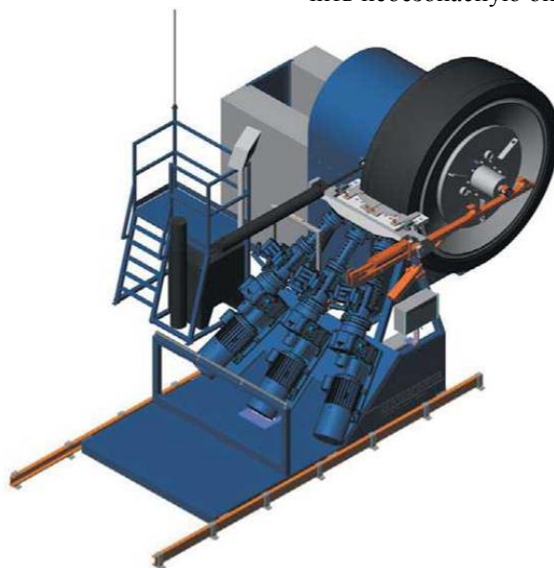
Опытный образец сборочного станка «Base Constructor для обрезинивания каркасов КГШ и СКГШ» фирмы VMI Group (Голландия).
